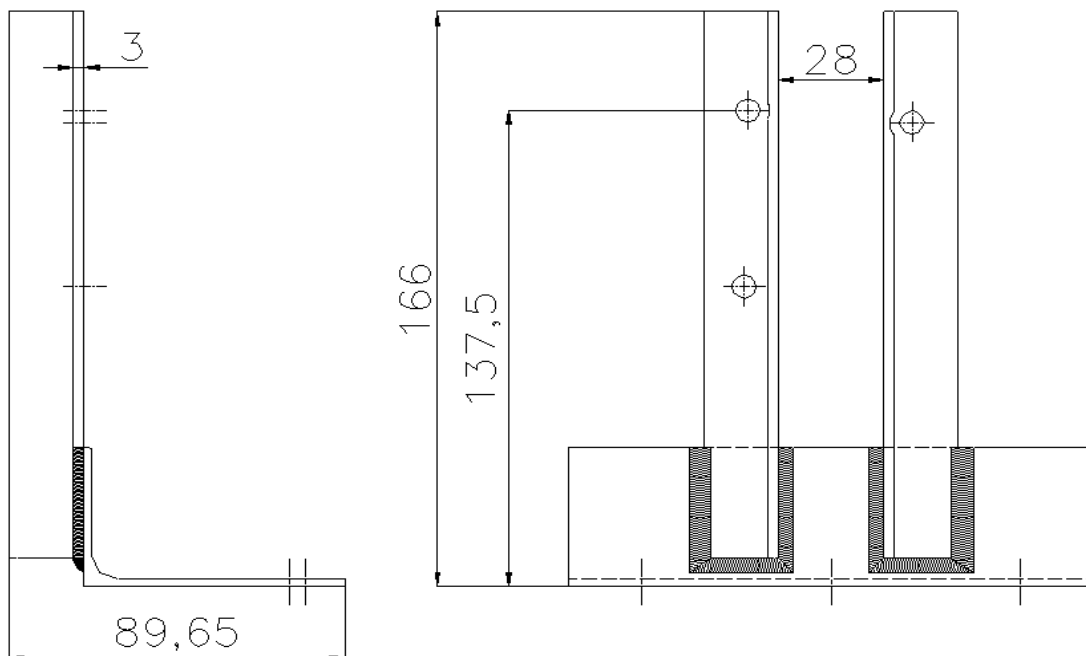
Dimensiones del soporte que sujetará al motorreductor
